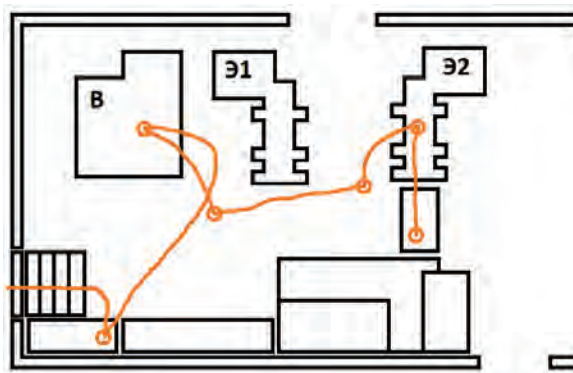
Планировка заготовительного участка с отображением перемещениями заготовки
